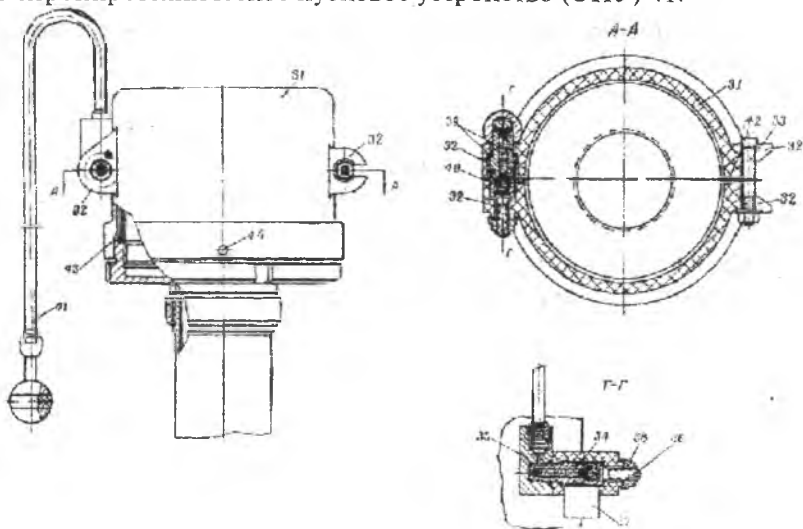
Защитное устройство взрывателя: 31- колпак; 32- ушки; 33- болт; 34- стяжная втулка; 35- приставка; 36- крепежная шпилька; 37- защитная скоба; 38- гайка; 39, 40, 42, 43- прокладки; 41- ЭПУ; 44- стопор
